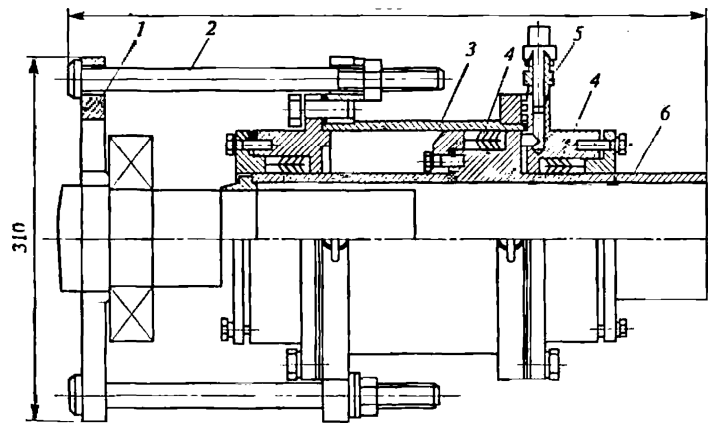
Гидравлический подвесной съемник для снятия подшипников валов двигателей с высотой оси вращения 180...280 мм (6...9-го габаритов): скоба; 2 - тяга; 3 - цилиндр; 4 - уплотнения; 5 - штуцер; 6-поршень
